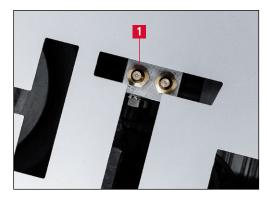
Schmiernippel am Schmierblock für die Kugelumlaufführungen
